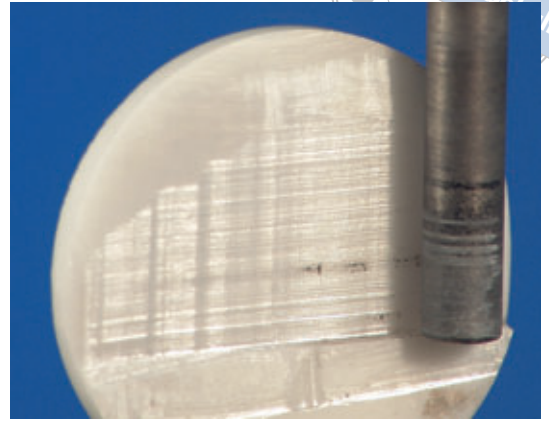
Auch wenn, wie bei dieser Schleifprobe, der Winkel zwischen Werkstück und Schleifer korrekt ist, so ist die nachfolgende Bearbeitung mit zu feinem Korn ein zu großer Schritt für die ZrO_2 -Oberfläche. Der punktuelle Angriff der ZrO_2 -Rillen auf den Schaft des Werkzeugs verschleißt dieses Werkzeug innerhalb von wenigen Sekunden.
